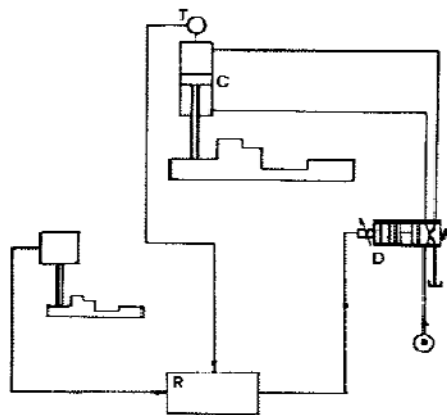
Comando di un tastatore per macchina utensile copiatrice
